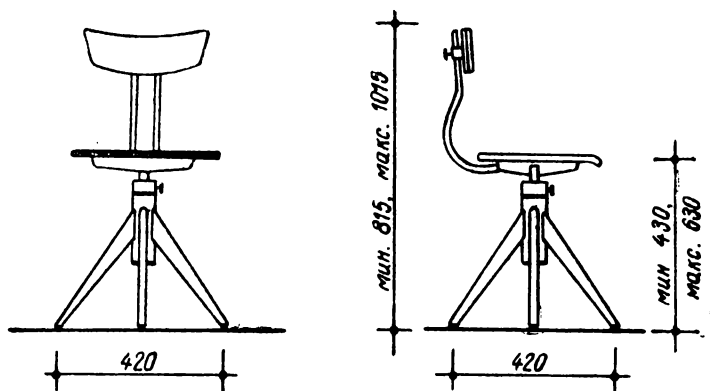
Подъемно-поворотный стул, тип. I.
